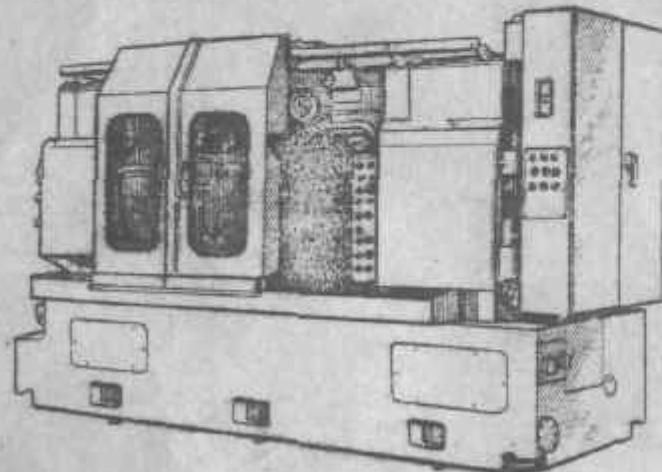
Полуавтомат токарный шестишпиндельный патронный горизонтальный мод. IB240P-6(6K)
